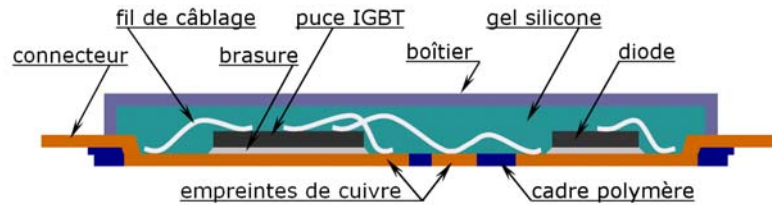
Illustration d'assemblage par Insert Molded Leadframe.
